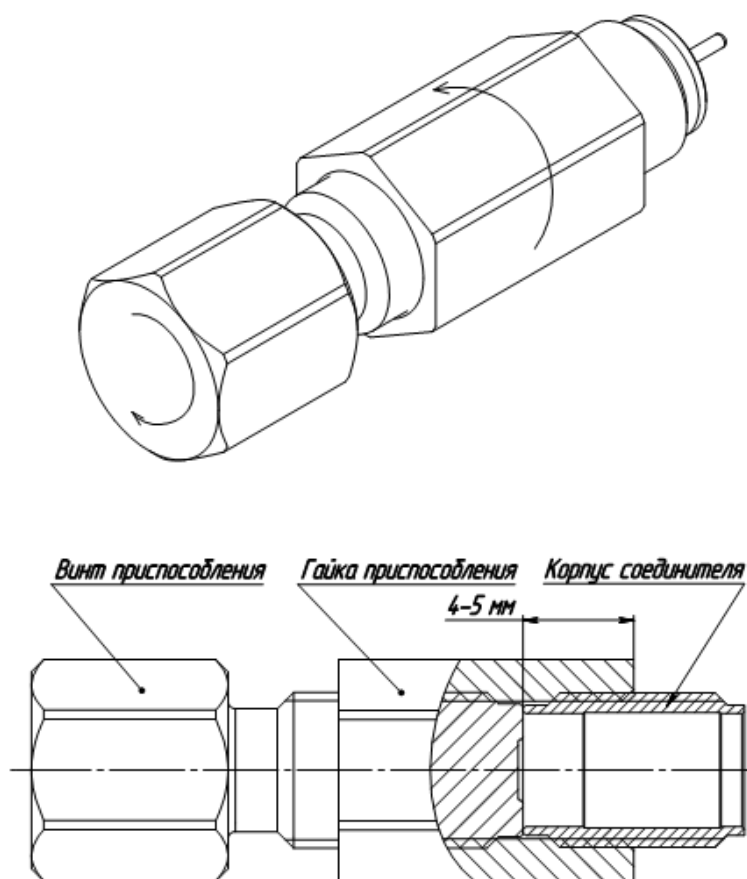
Установка корпуса в приспособление 7290-0214.00.000.00-02
